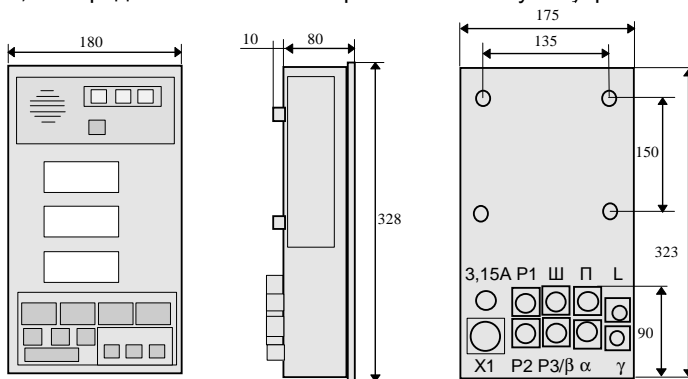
Габаритные и присоединительные размеры БОДа
